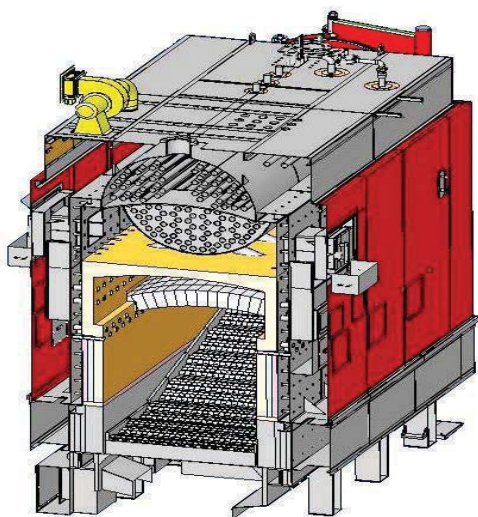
Конструкція твердопаливного біокотла «Комконт» СН COMPACT
